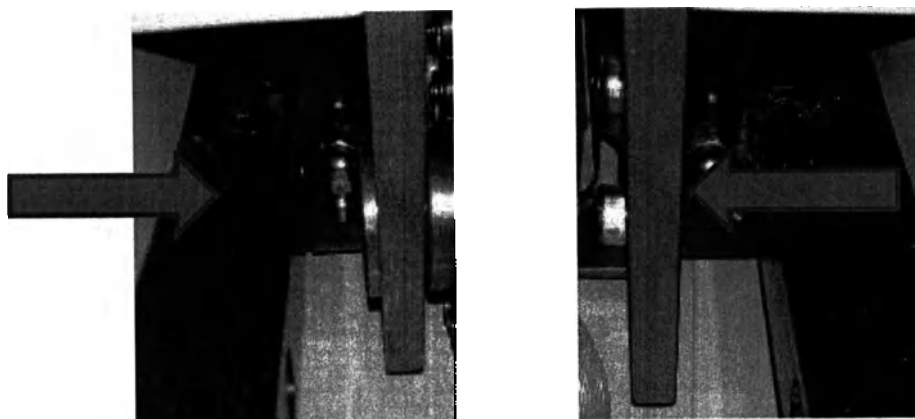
Пресс-масленки линейных подшипников направляющих
